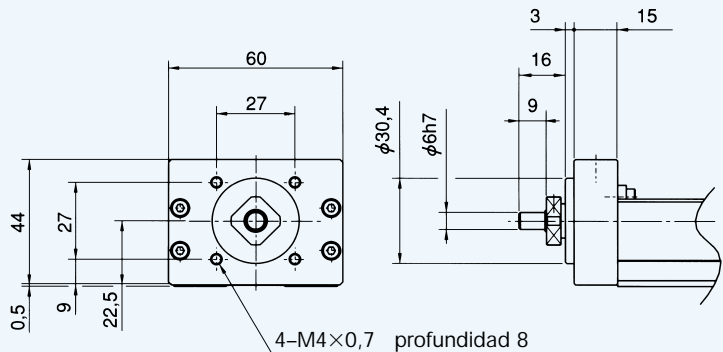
■ KR33 Adaptador A sin brida de motor (indicativo 40).
